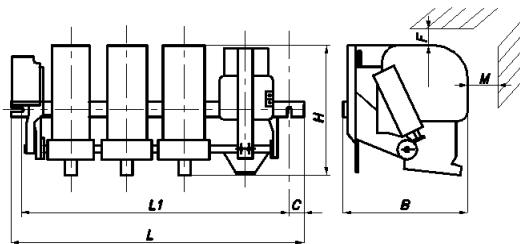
Общий вид и габаритные размеры КТ-6000.
